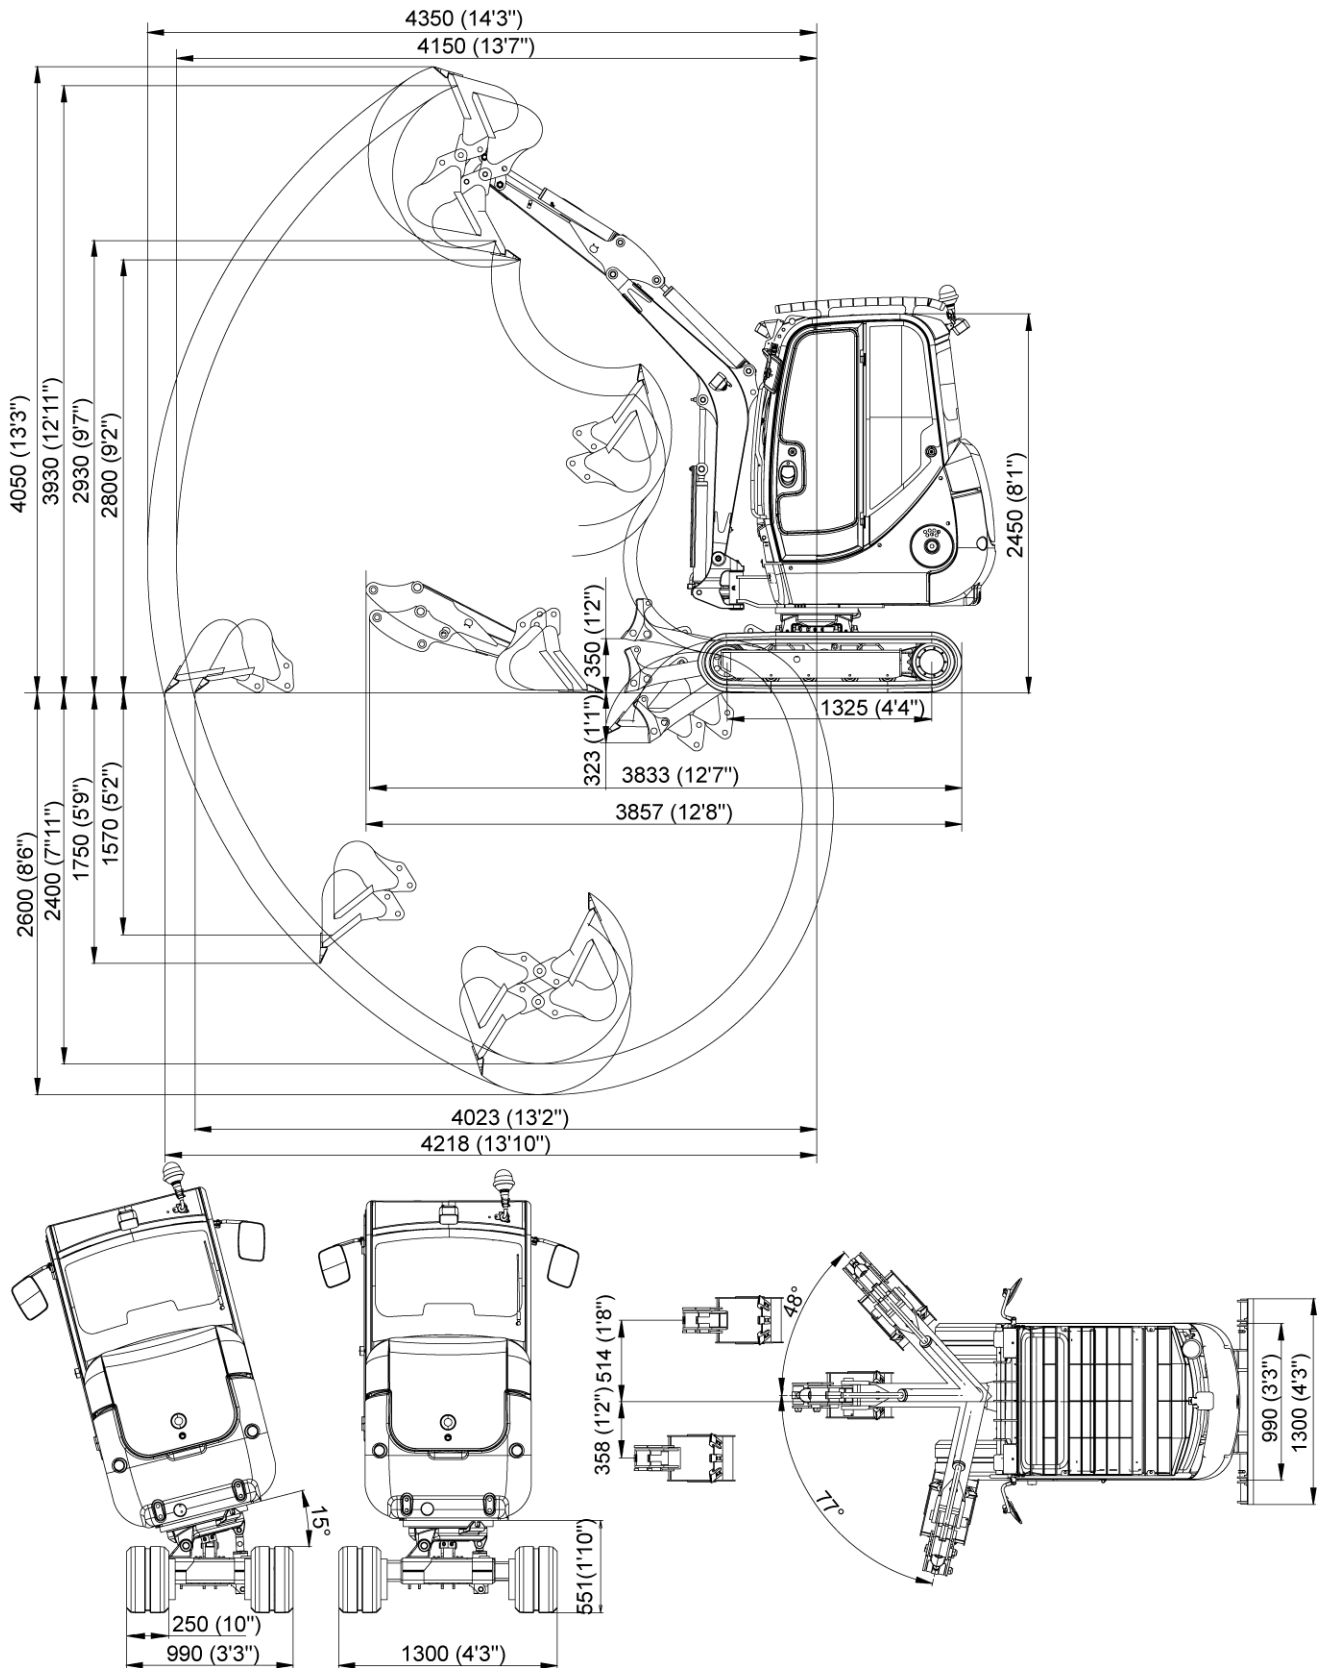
Køretøjets dimensioner (type 2003 VDS)
